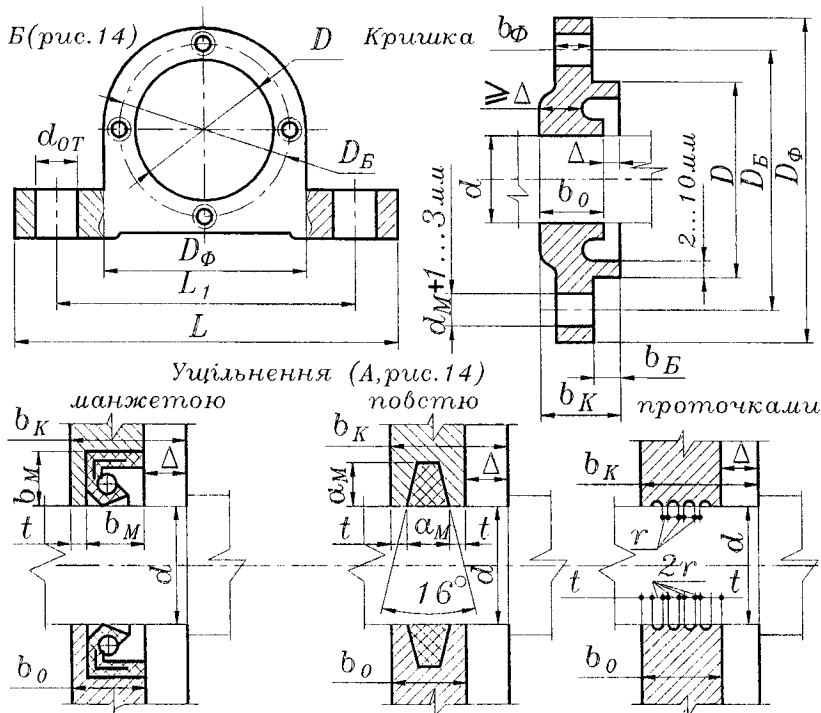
Елементи конструкції підшипникових вузлів приводного вала
